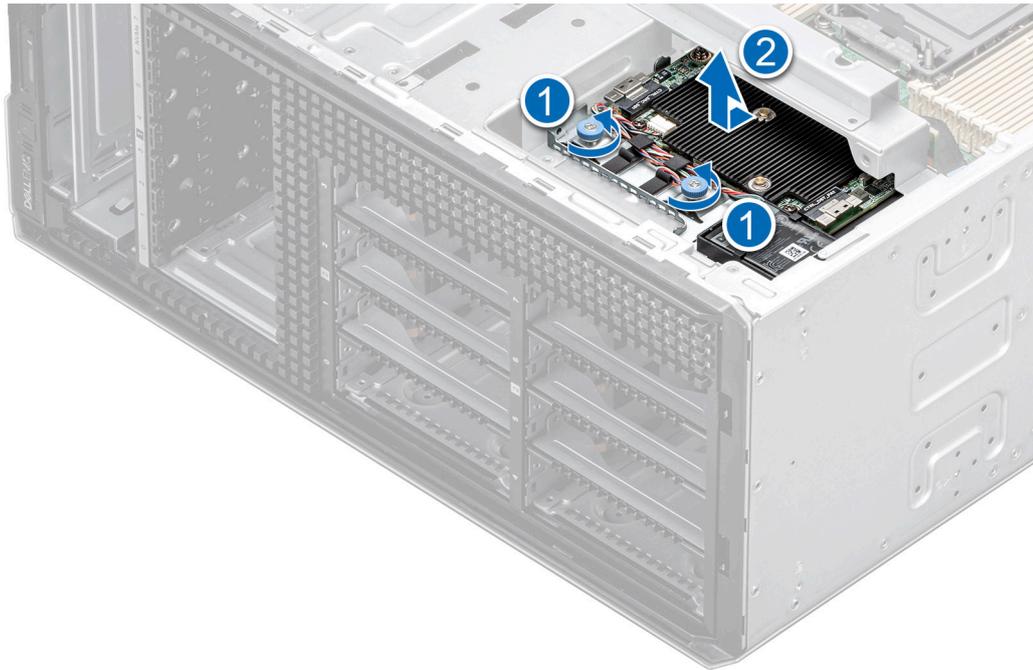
Entfernen des PERC-Frontmoduls für eine 3,5-Zoll-Laufwerkrückwandplatine
